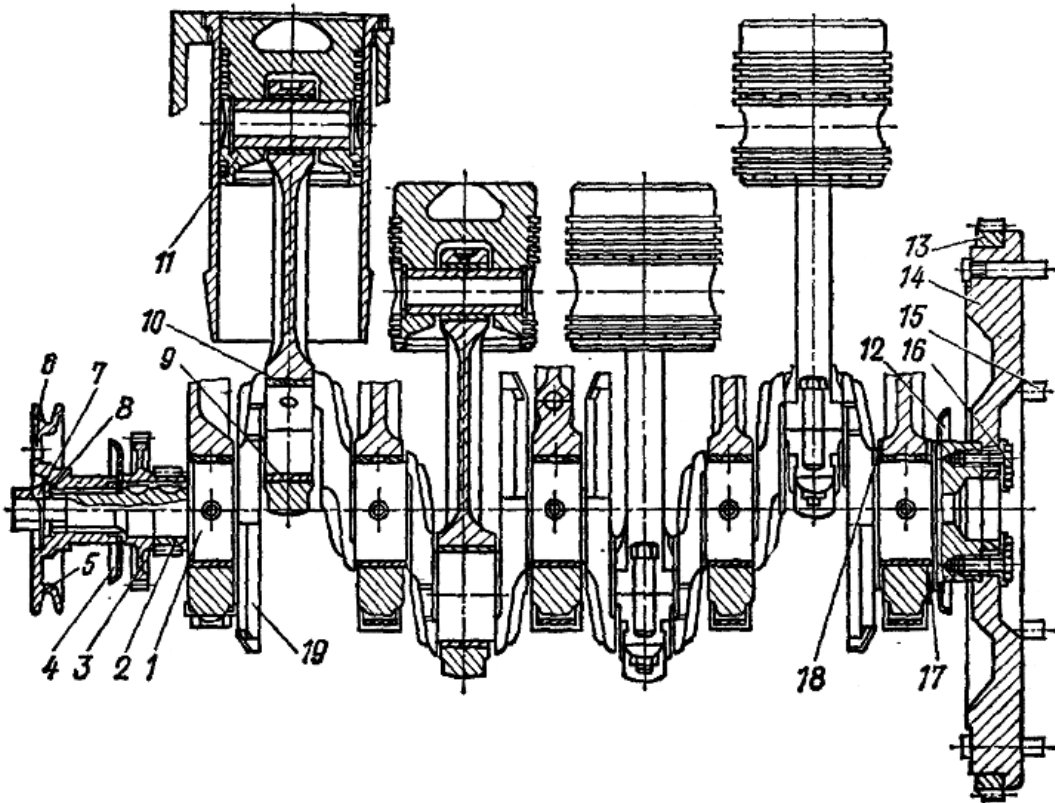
Кривошипно-шатунный механизм двигателя Д-240:
